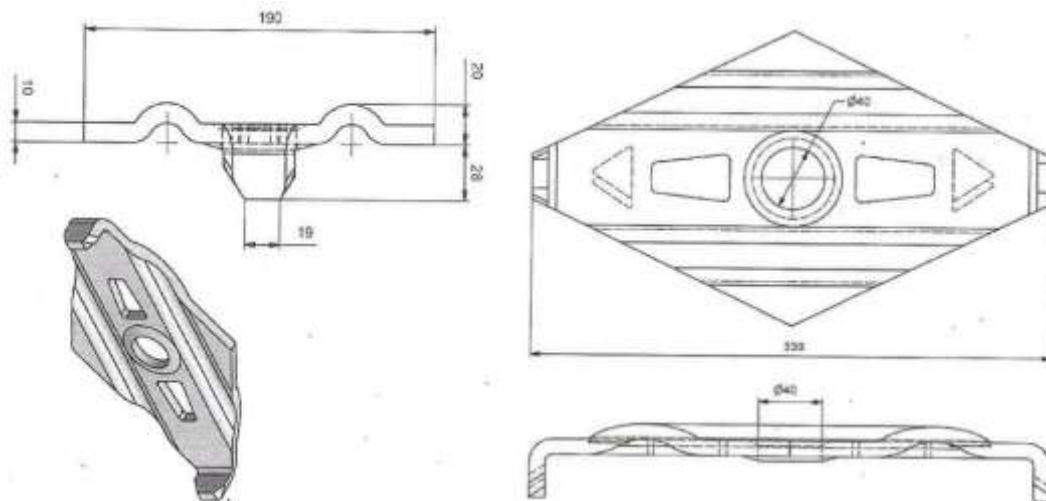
Dimensiones de la placa de fijación del sistema TECCO® (Geobrugg A Company of the BRUGG Group)
